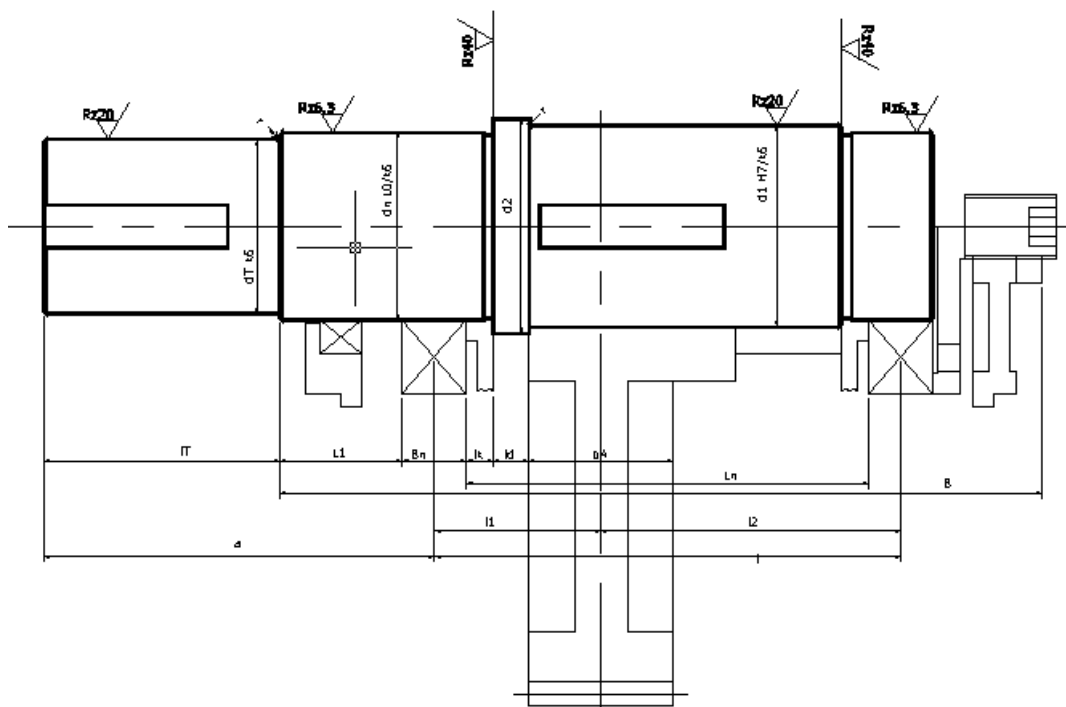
Назначение размеров, посадок и шероховатостей тихоходного вала
